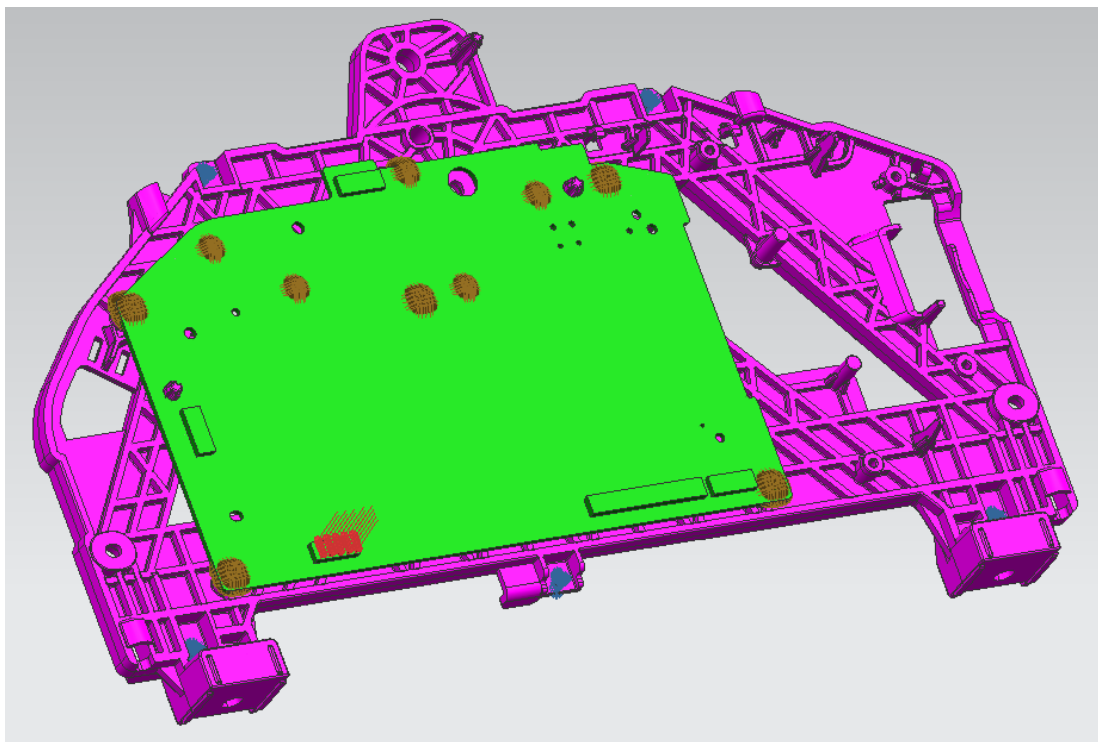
Contactos entre *supporting plate* e PCB.
